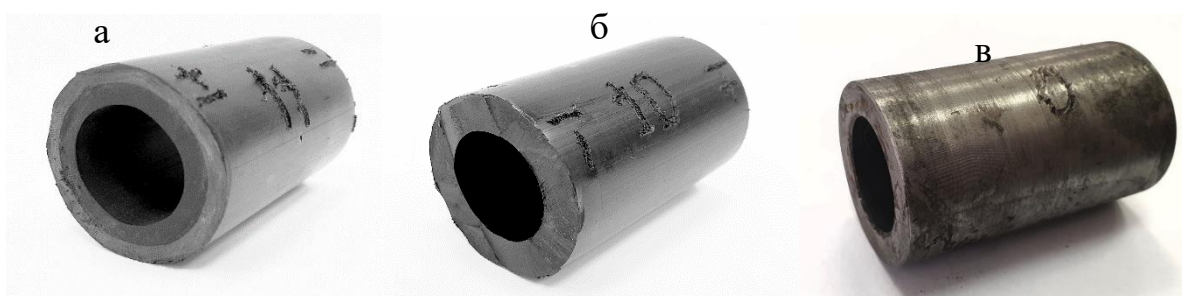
Испытываемые образцы: а – образец № 1, б – образец № 2, в – образец № 3
